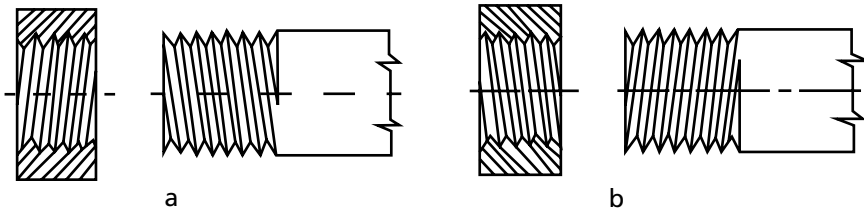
Tornillos: a) rosca derecha; b) rosca izquierda
